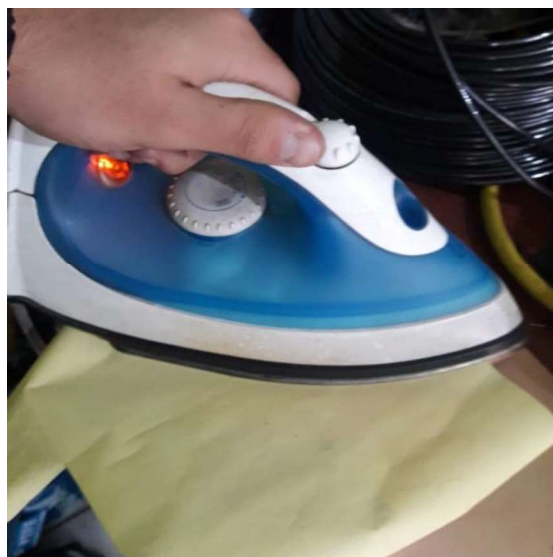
Transferencia de tóner en la placa mediante planchado.
